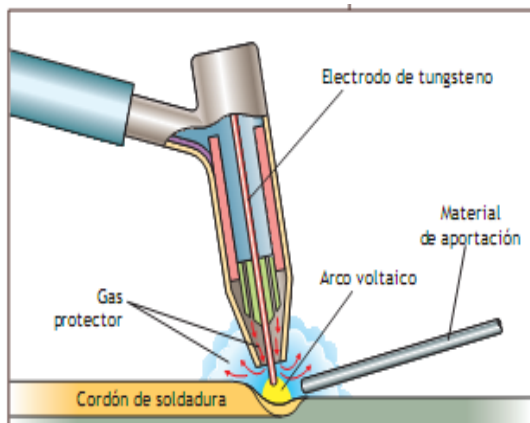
Proceso de soldadura GTAW. Fuente: Méndez y Eagar (2001).
